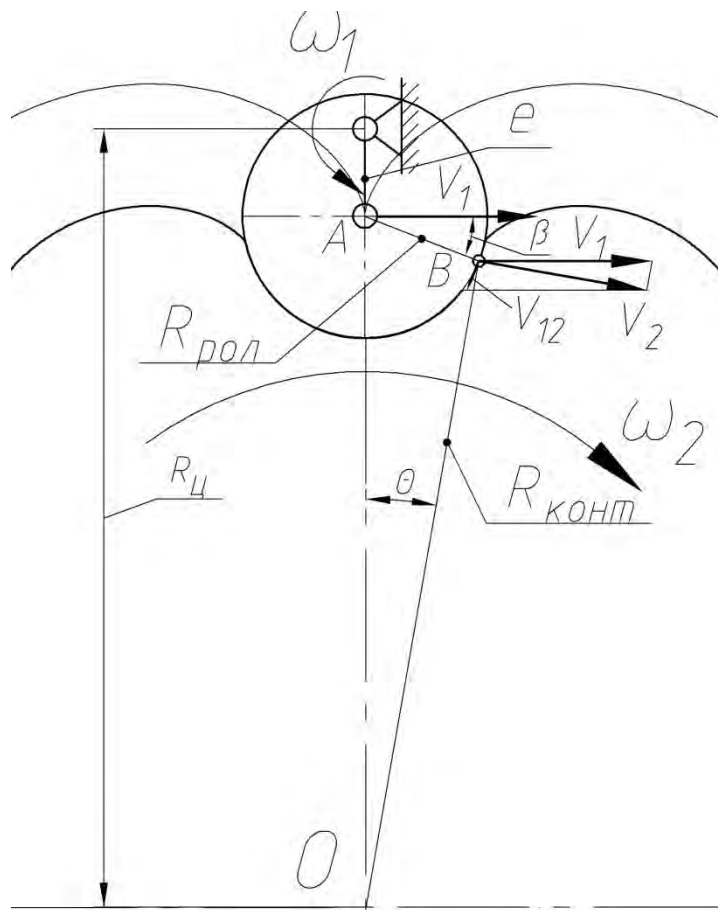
Схема формообразования поверхности зубьев сателлитного колеса
